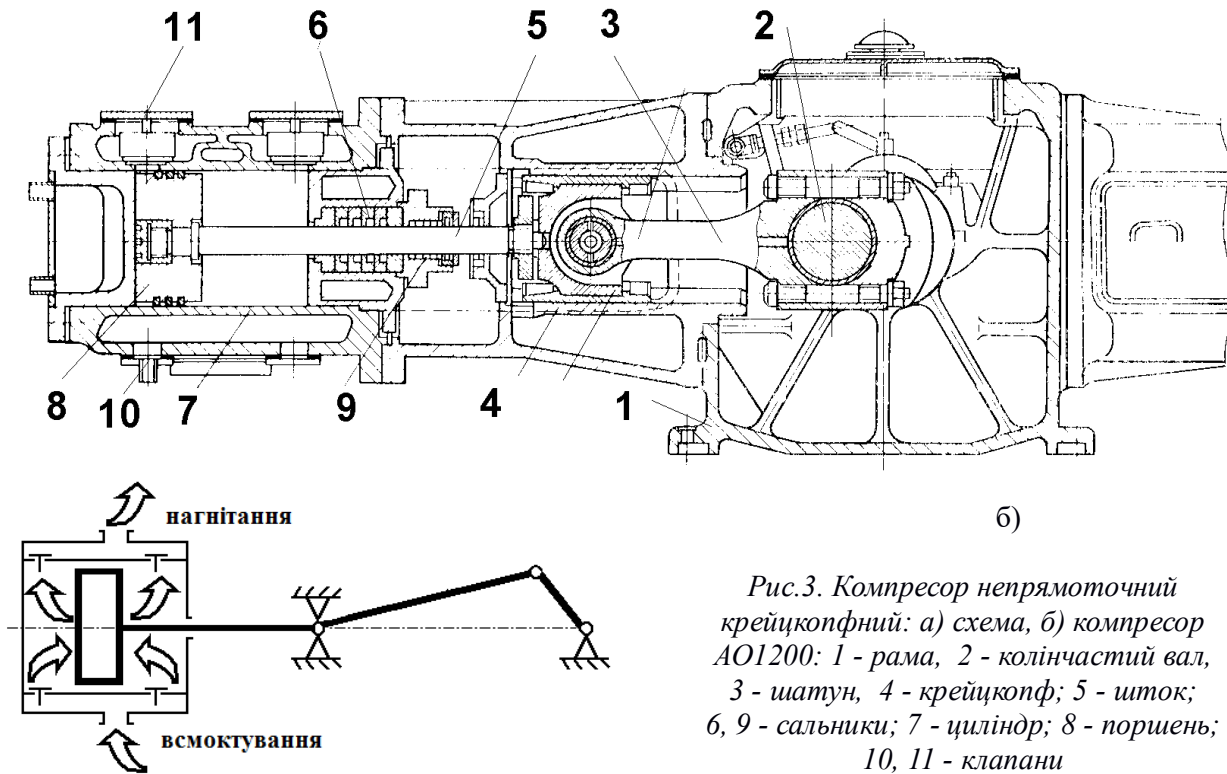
Компресор непрямоточний кривокопфний: а) схема, б) компресор АО1200: 1 - рама, 2 - колінчастий вал, 3 - шатун, 4 - кривокопф, 5 - шток; 6, 9 - сальники; 7 - циліндр; 8 - поршень; 10, 11 - клапани
